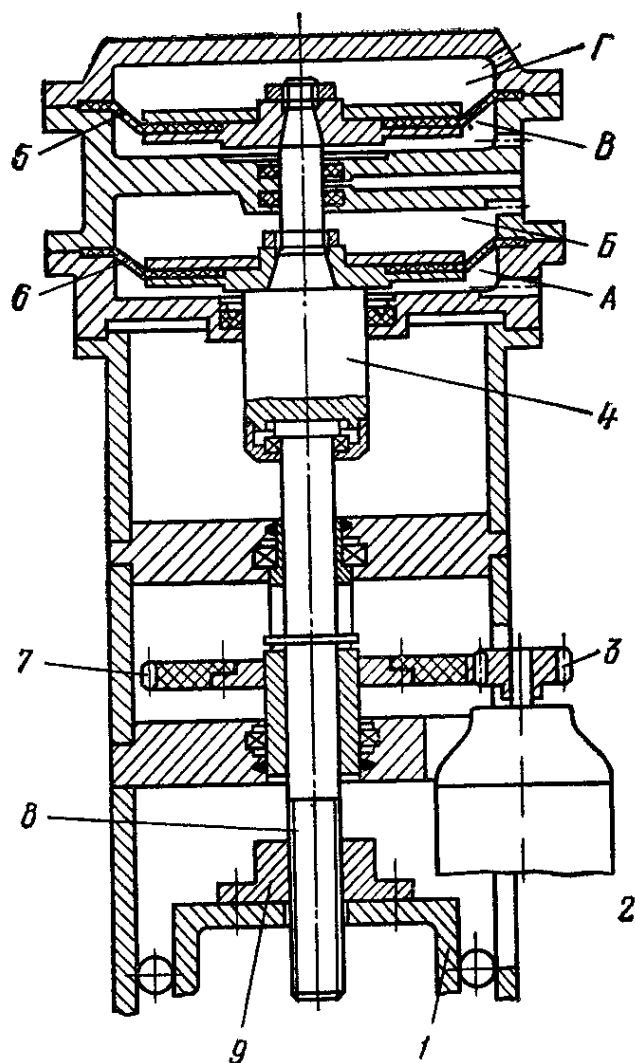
Диафрагменный привод сжатия и электродвигательный дополнительный хода машины МТВ-6304:
